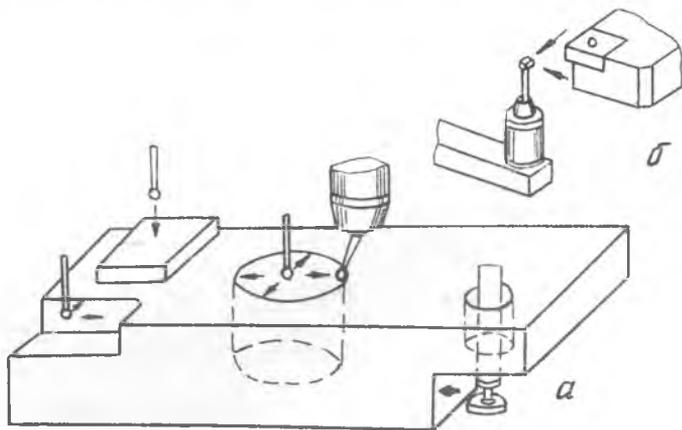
Схемы измерений обрабатываемой детали (а) и режущего инструмента (б) шупами
